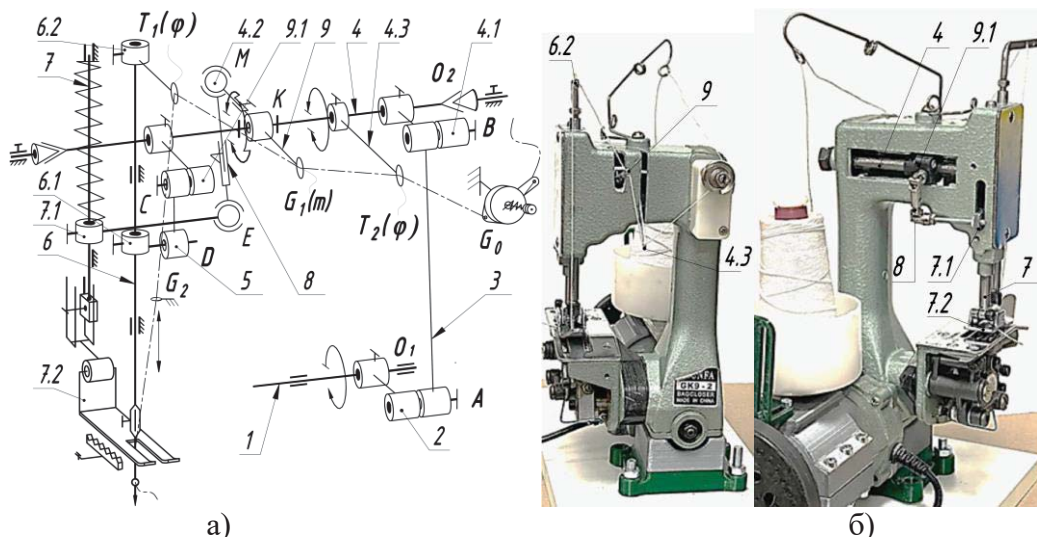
Механізм подачі нитки швейної машини: а) кінематична принципова схема, б) загальний вигляд конструкції
